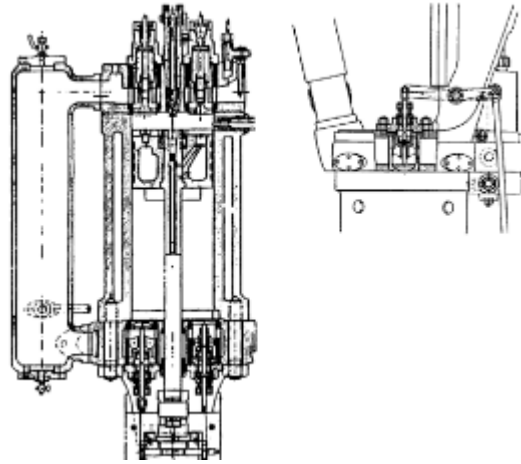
Patente DRP 95680 de Rudolf Diesel para motor diésel con sistema de sobrealimentación acoplado a cada pistón.
